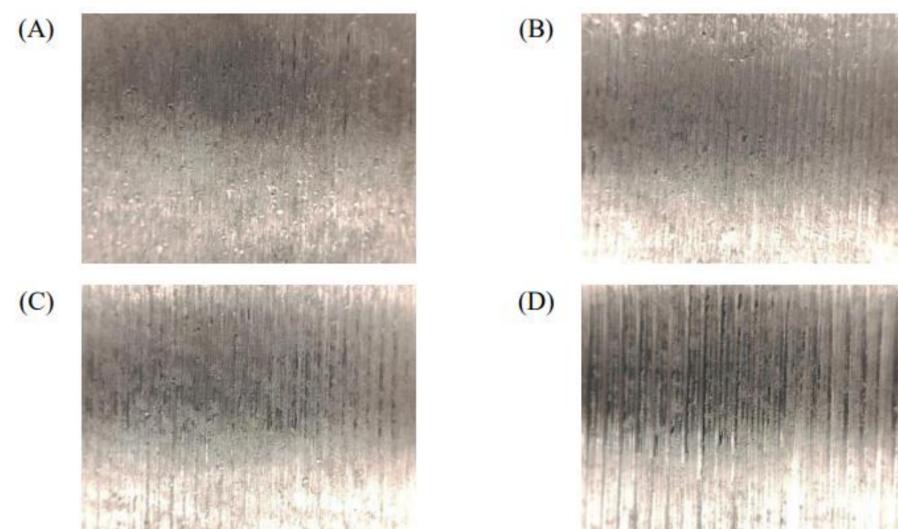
Imagens tiradas da peça usinada com  $V_c = 120\text{ m/min}$  e diferentes avanços (A) Superfície usinada com avanço  $f = 0,10$ , (B) Superfície usinada com avanço  $f = 0,15$ , (C) Superfície usinada com avanço  $f = 0,20$  e (D) Superfície usinada com avanço  $f = 0,25$
